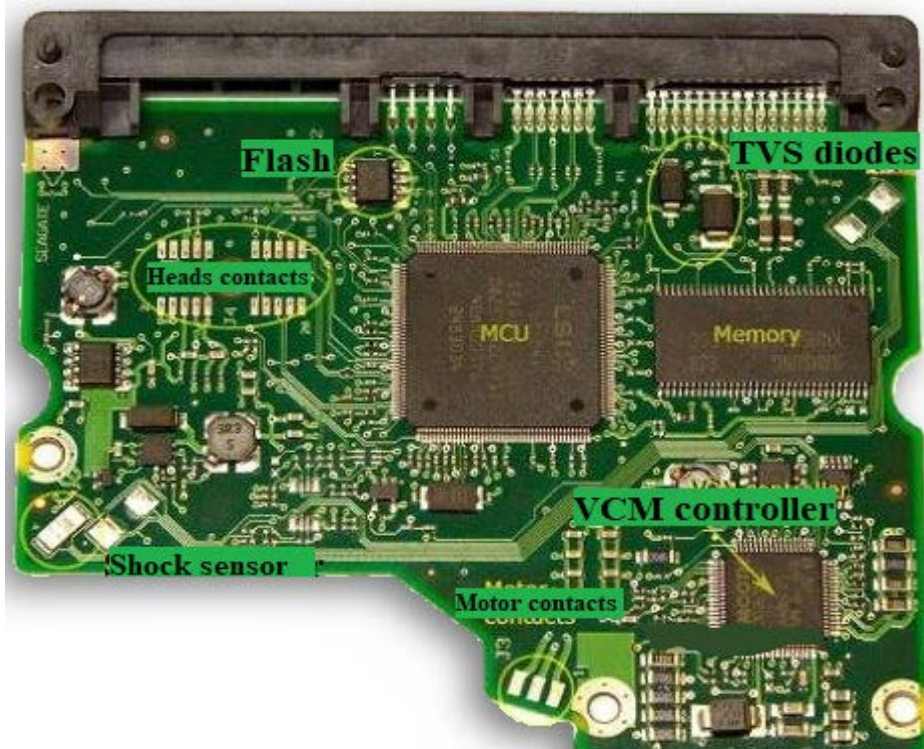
PCB HDD, де Heads contacts - контакти головок, Motor contacts – контакти моторчиків
